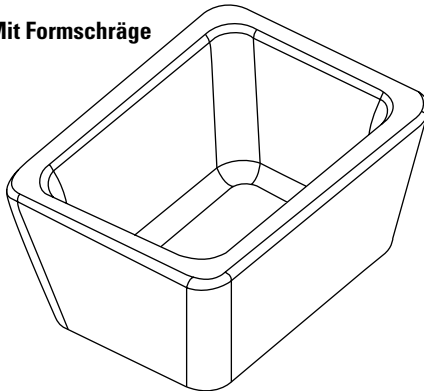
Beispiel für eine Formschräge beim Spritzgießen.
